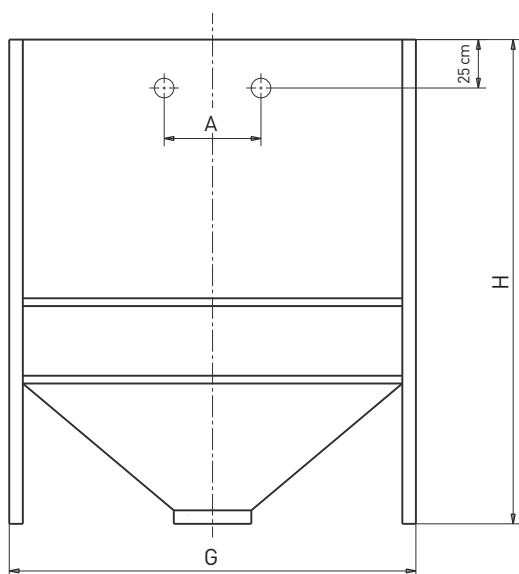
Aufstellfläche für Gewebe-Tank GET 251
